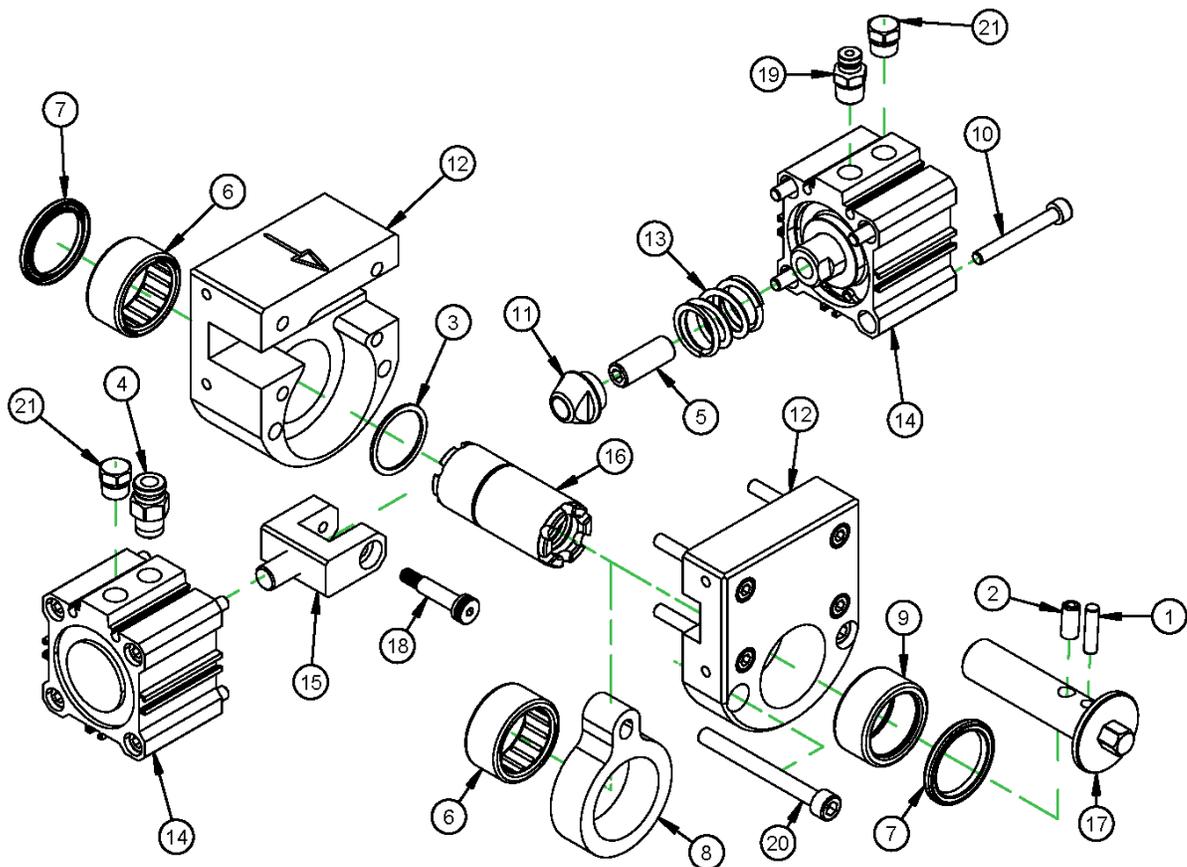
PORTABROCAS DI/DE 45-120" PARA TORNEAR CON CONJUNTO DE BRAZO FRESADOR (N/P 62666)
